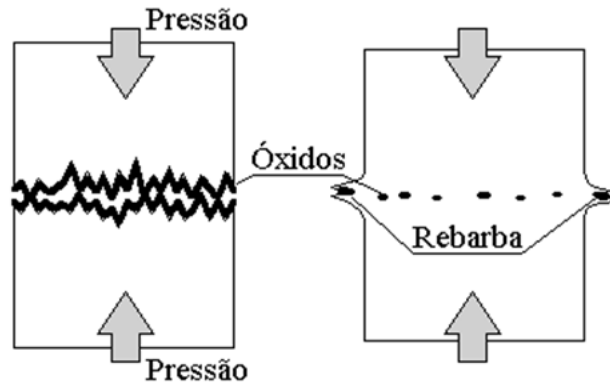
Modelo de soldagem por pressão <sup>(3)</sup>.
